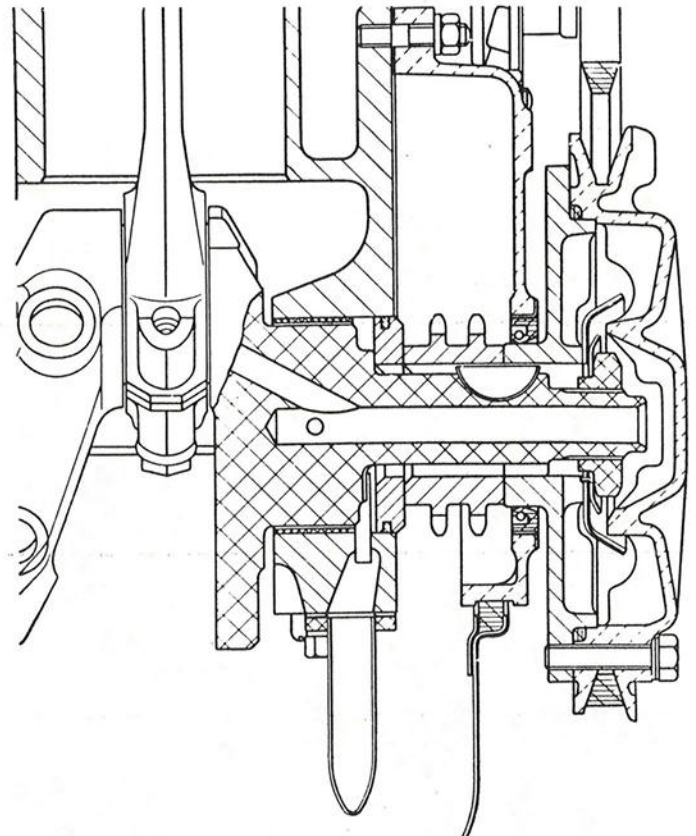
Längsschnitt des Motors (Detail des Ölschleuderfilters).
